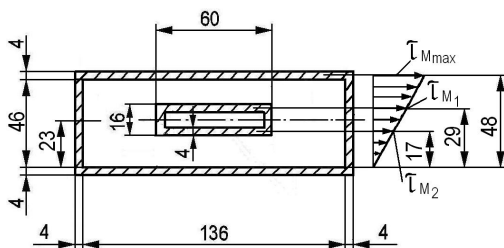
Расчетное сечение сварных швов и эпюра напряжений от момента
